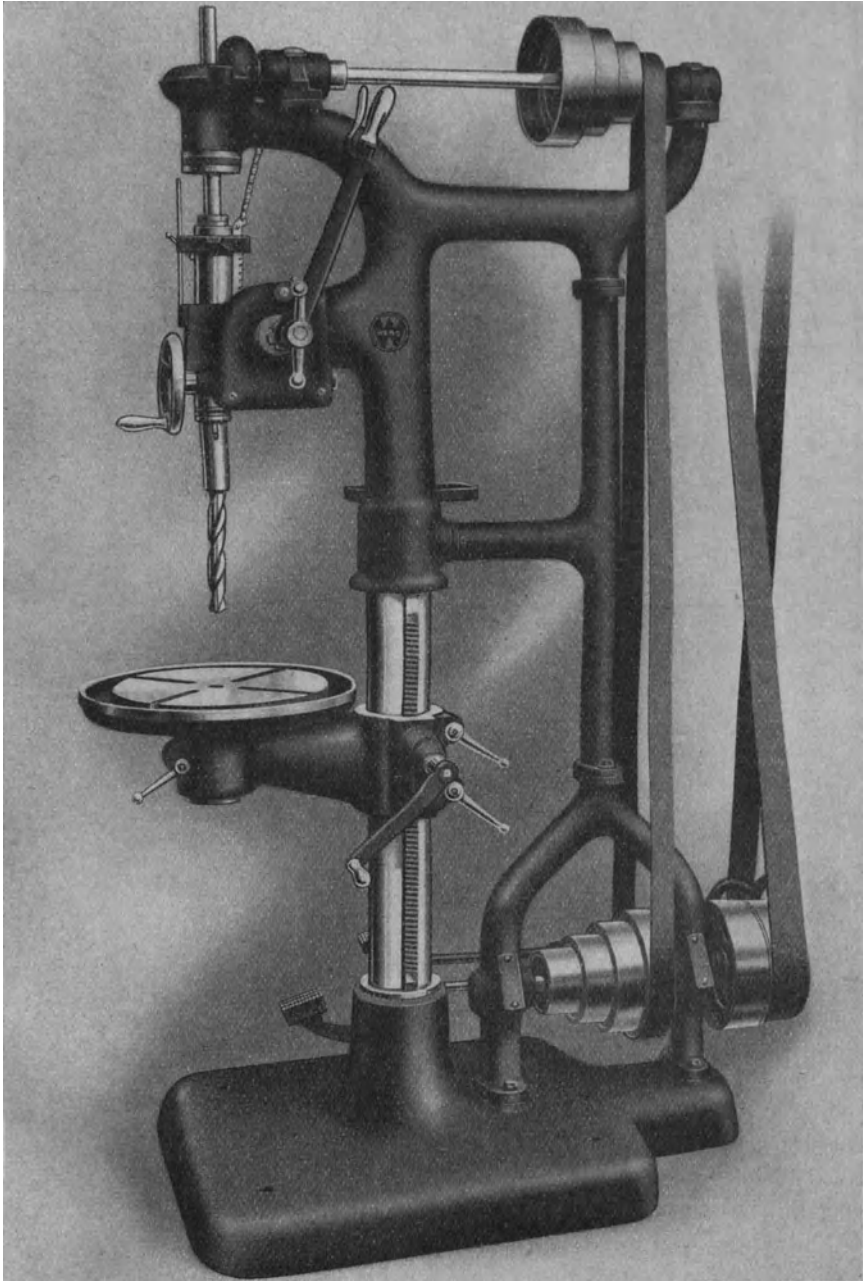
Senfrccht-Bohrmaschine der Debo.
